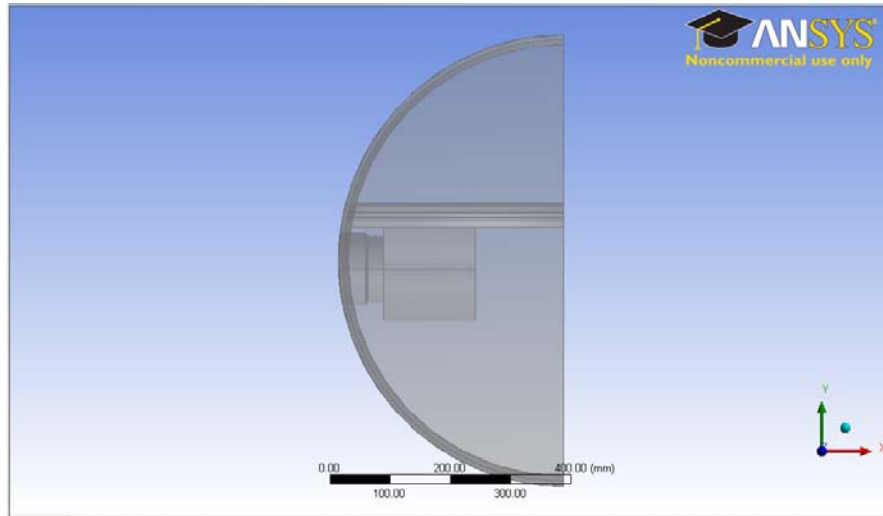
Vista de la geometría de estudio con la tubería en el plano XY [Material propio]
